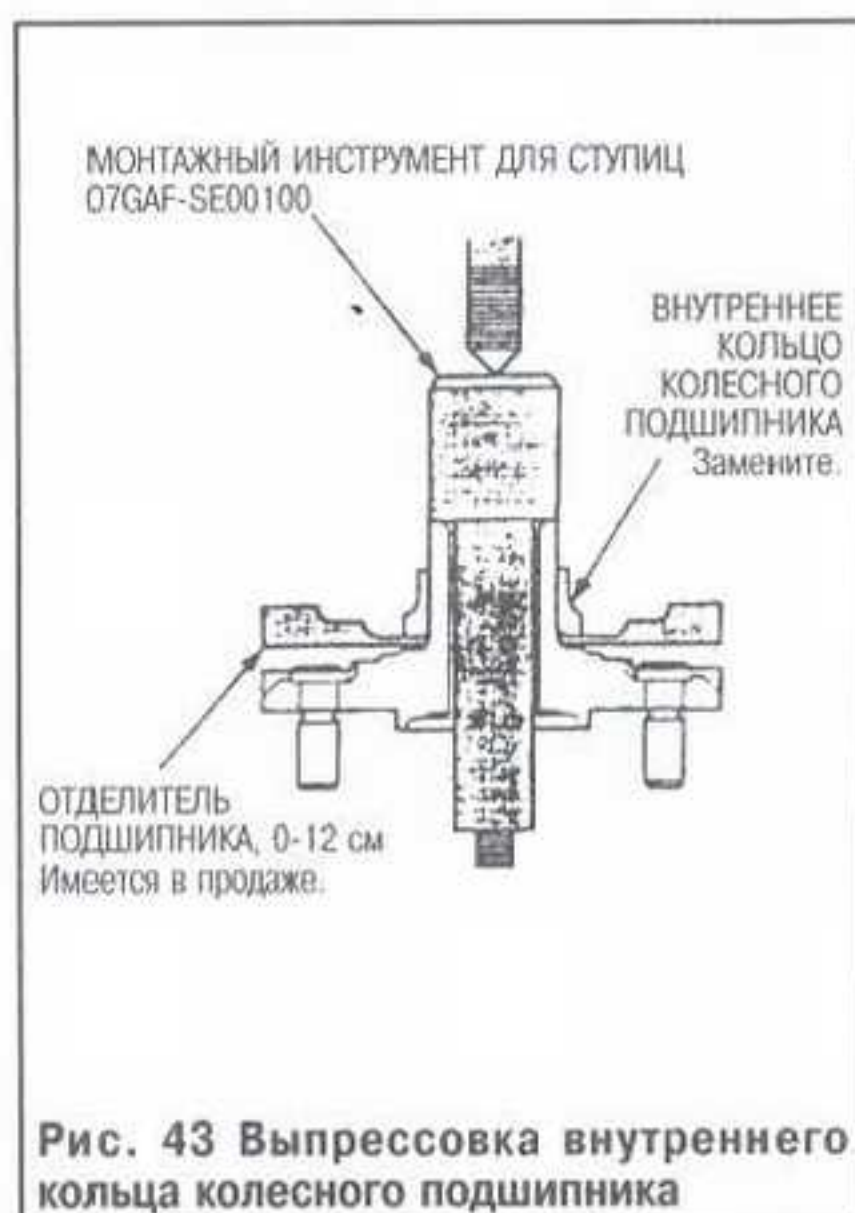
Выпрессовка внутреннего кольца колесного подшипника
